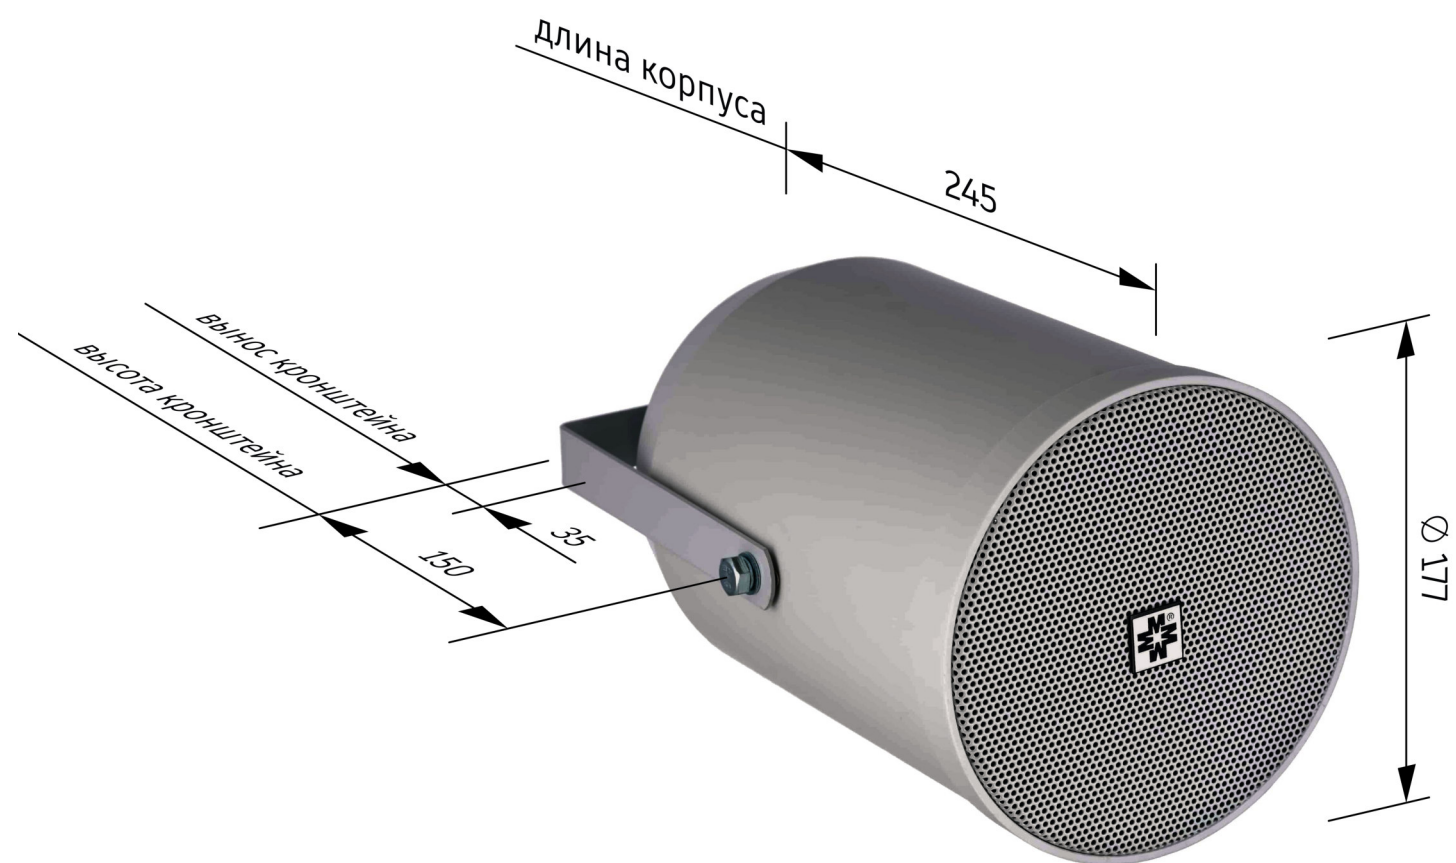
Габаритные и установочные размеры прожектора звукового META-7663.
